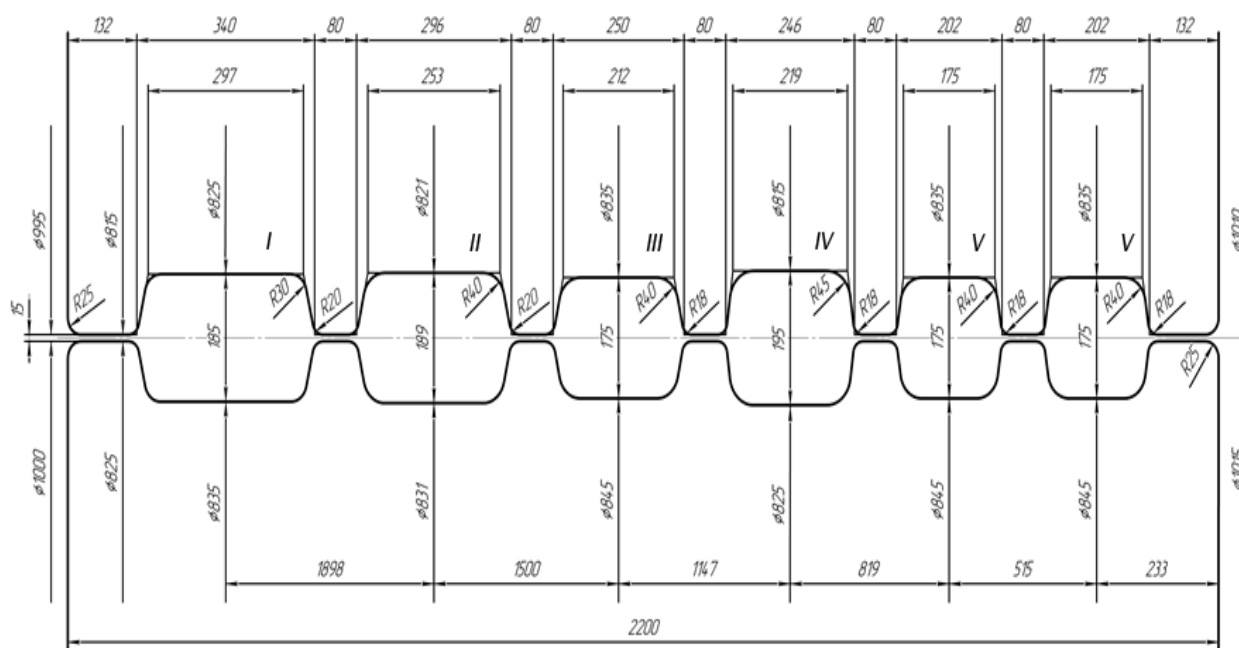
Расположение калибров валков реверсивной клетки дуо 1000
